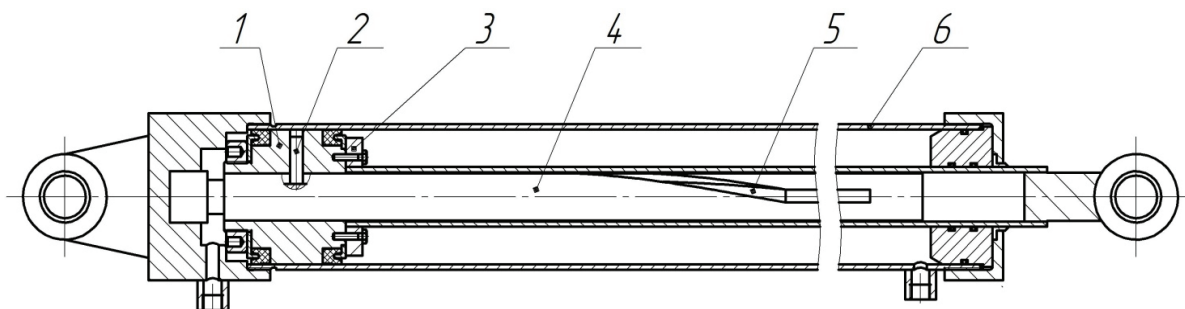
Схема гидроцилиндра перемещения выдвижной балки выносной опоры: 1 – поршень; 2 – штифт; 3 – фланец; 4 – направляющая; 5 – винтовая проточка; 6 – шток.
